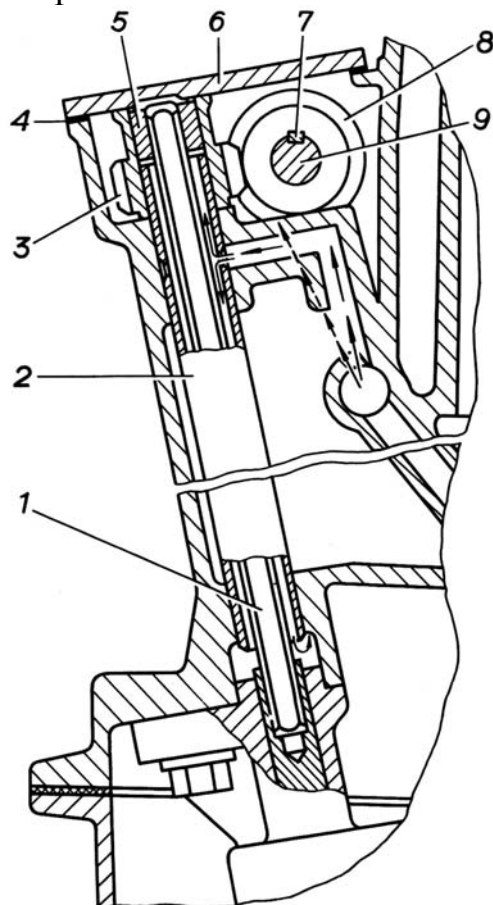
Привод масляного насоса: 1 - валик привода масляного насоса; 2 - валик; 3 - ведомая шестерня; 4 - прокладка; 5 - втулка; 6 - крышка; 7 - шпонка; 8 - ведущая шестерня; 9 - промежуточный вал
